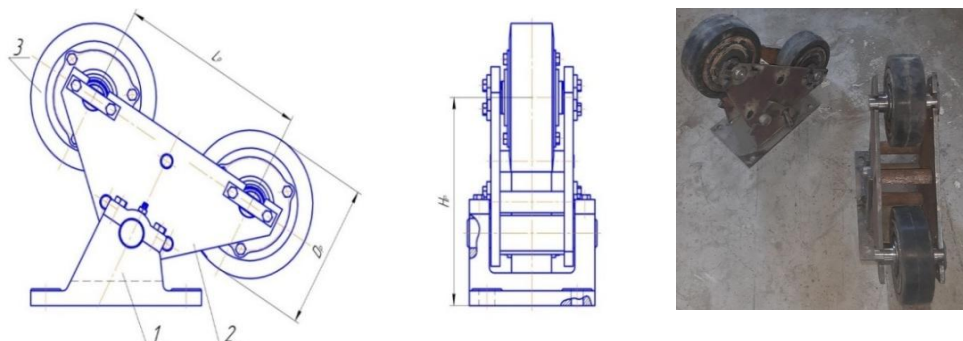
Схема ходовой части барабана сушилки и её внешний вид в собранном виде
